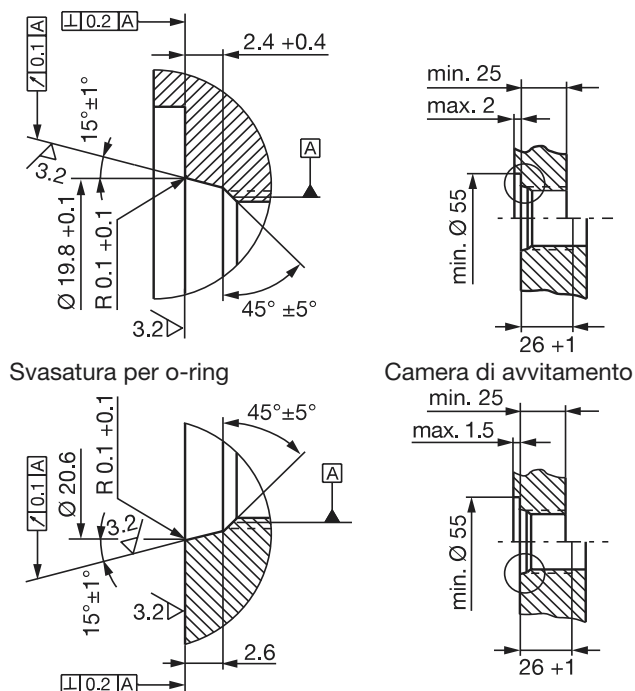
Camera di avvitamento per il montaggio del trasduttore BTL con o-ring
